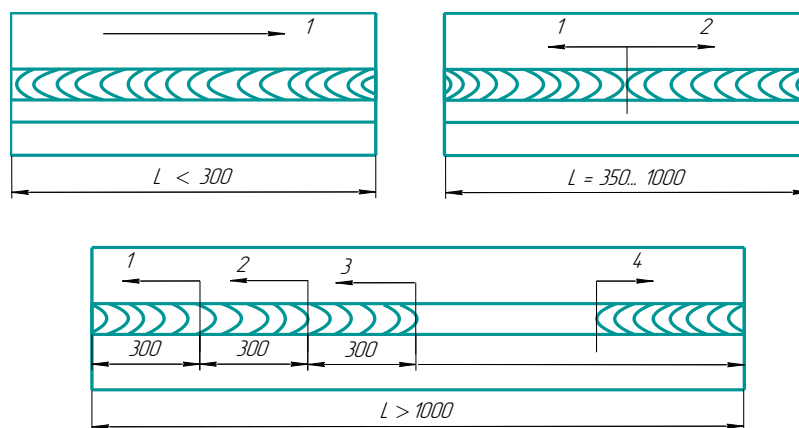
Схема выполнения сварочного шва по длине детали:
